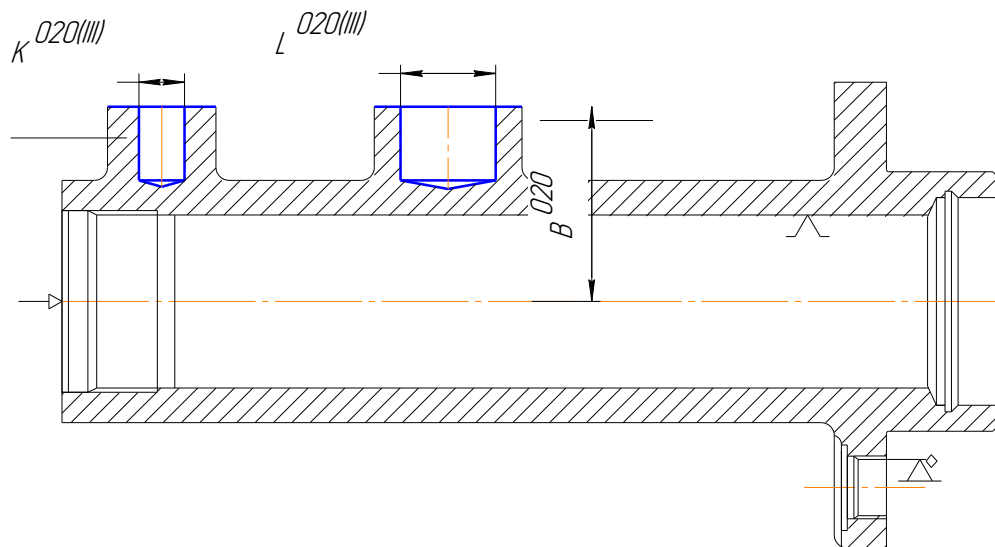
Получистовое и чистовое фрезерование торцов бобышек, сверление двух отверстий
